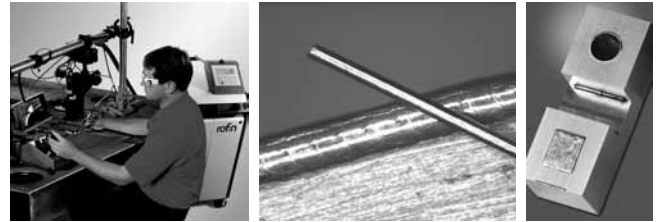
Manuelles Auftragschweißen (Quelle: Rofin Lasertechnik; Hamburg)
